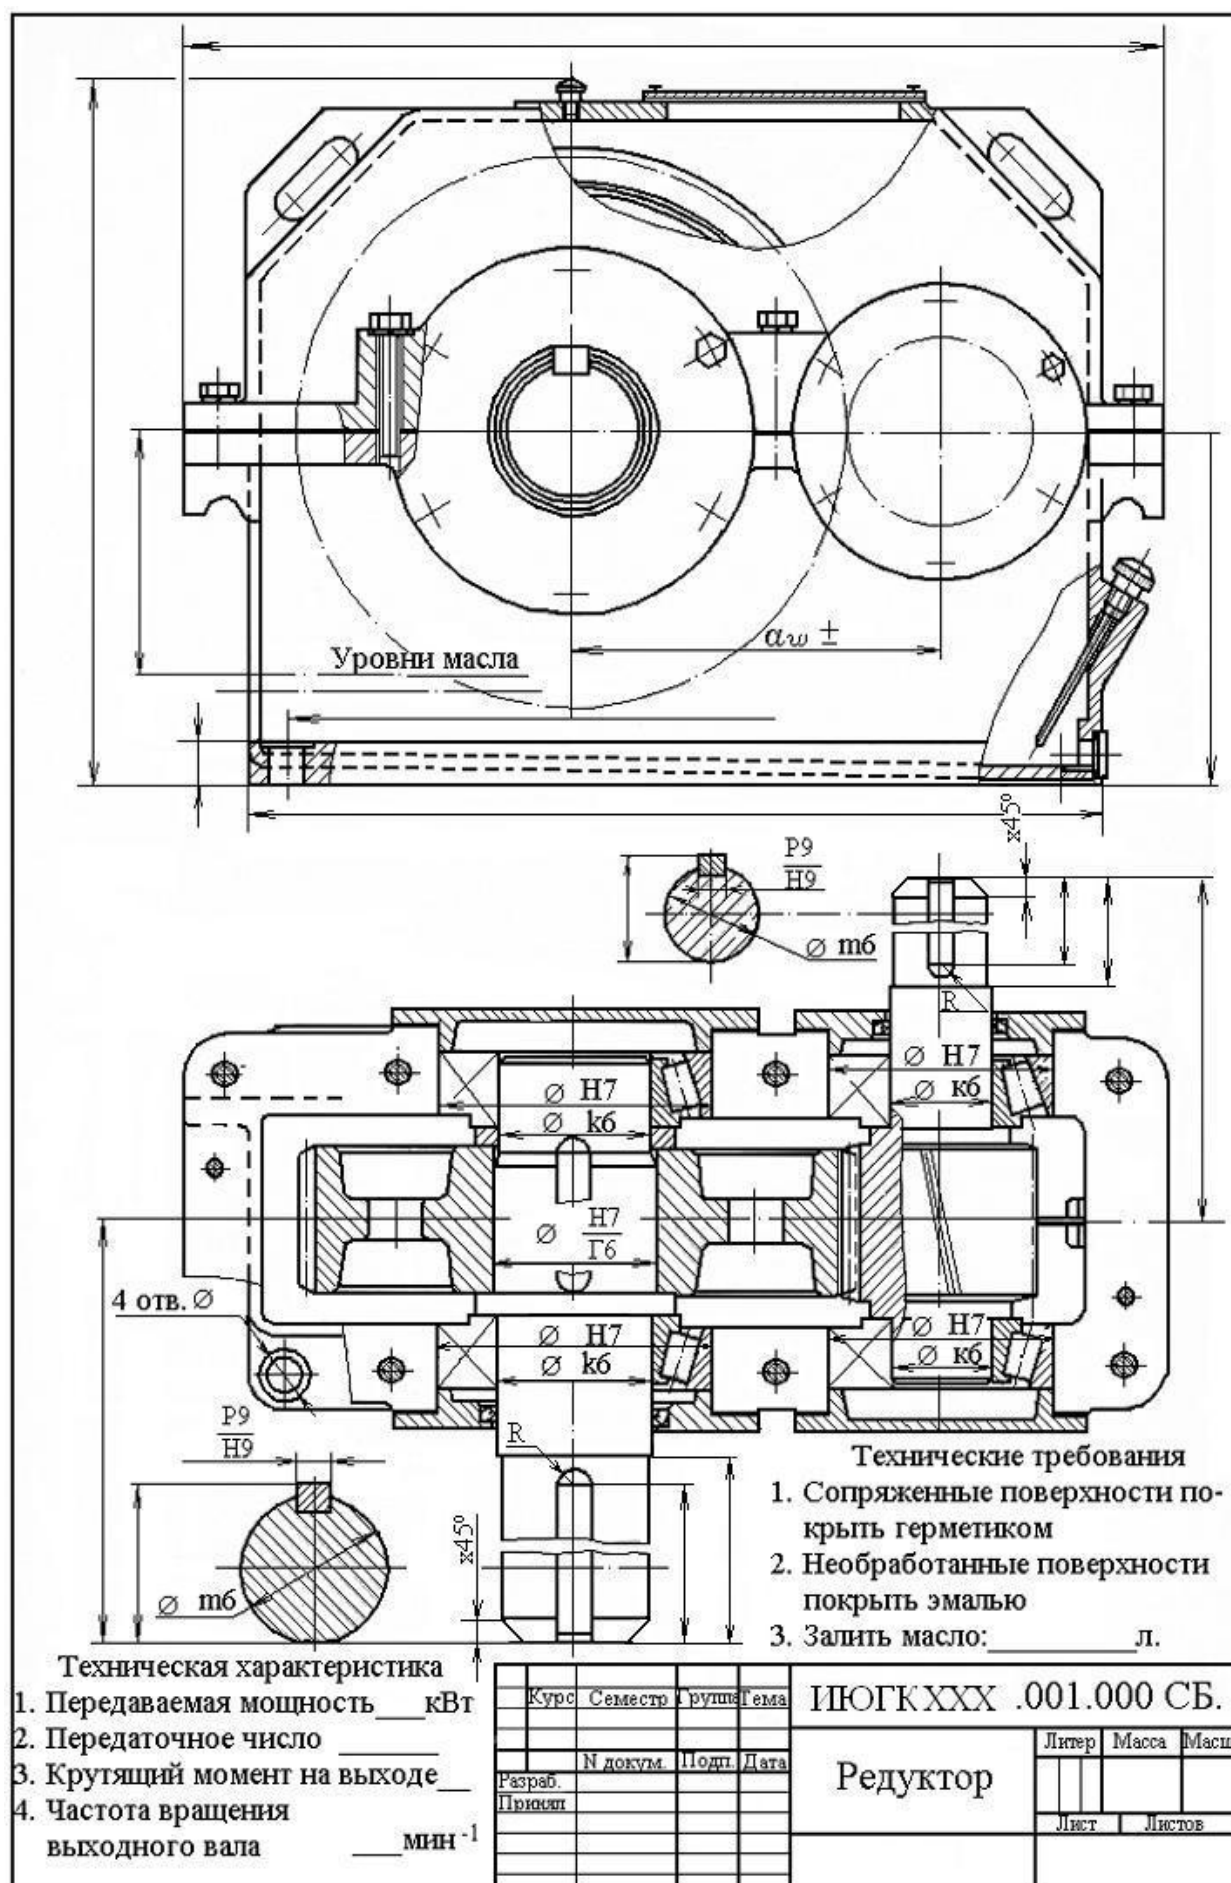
Редуктор цилиндрический одноступенчатый
